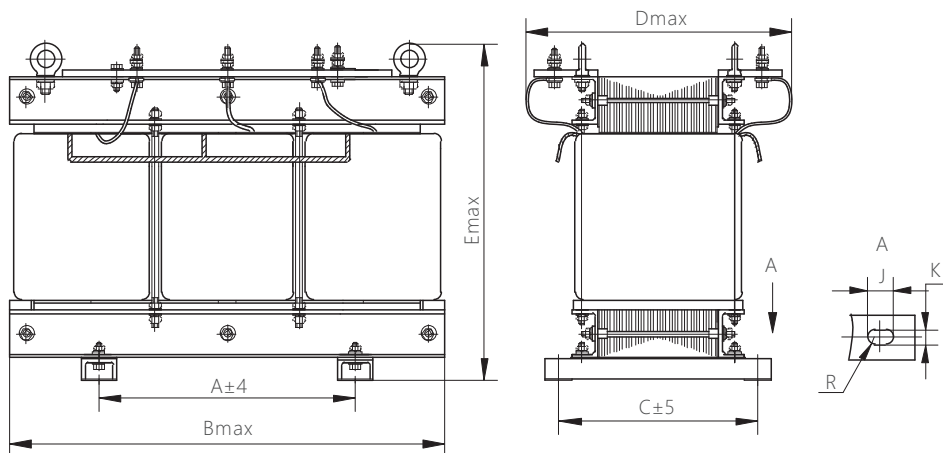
SCBK-30~100开启式外形尺寸与安装尺寸示意图
